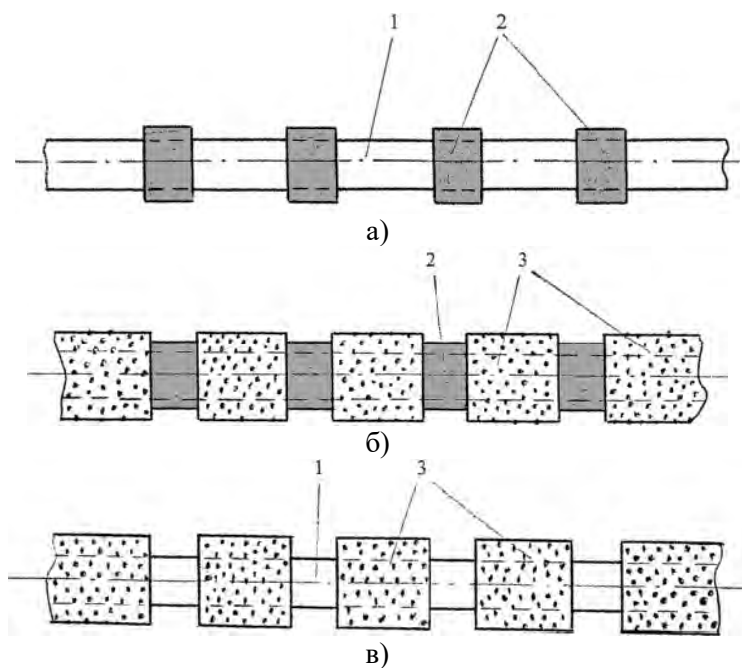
Этапы получения дискретных цилиндрических режущих элементов на проволоке: 1 – основа; 2 – дискретные элементы; 3 – режущий слой
